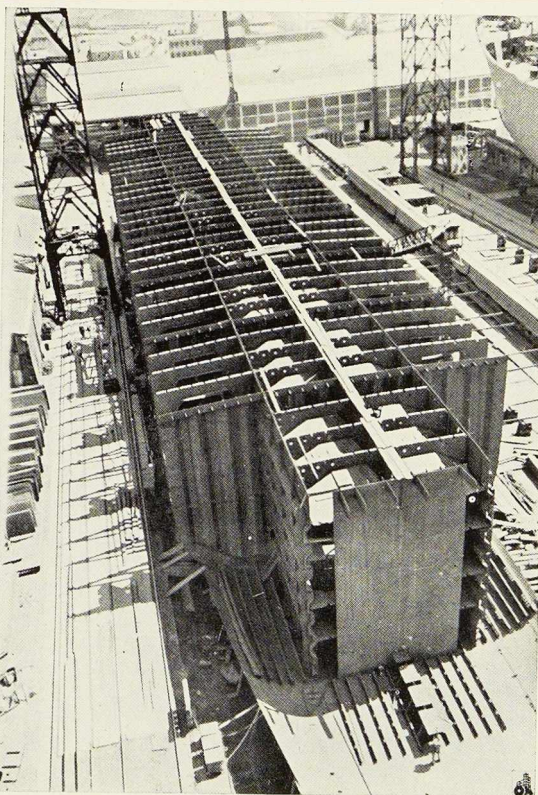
Perspective des cloisons d'un pétrolier de gros tonnage construit en tôles au profil « Palplanche » et assemblé par soudage (chantier John Cockerill).
